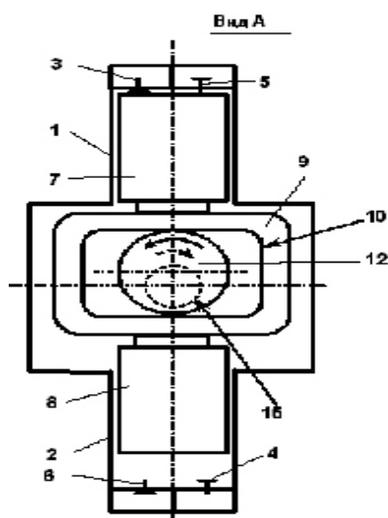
Схема поперечного сечения конструкции оппозитного компрессора с совмещенными электродвигателями (положение блока поршней «посередине»)
